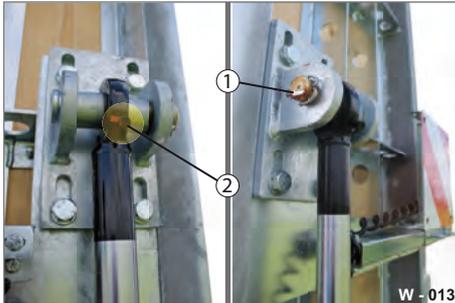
Obere Lagerstelle Auffahrampen, Hydraulikzylinder
